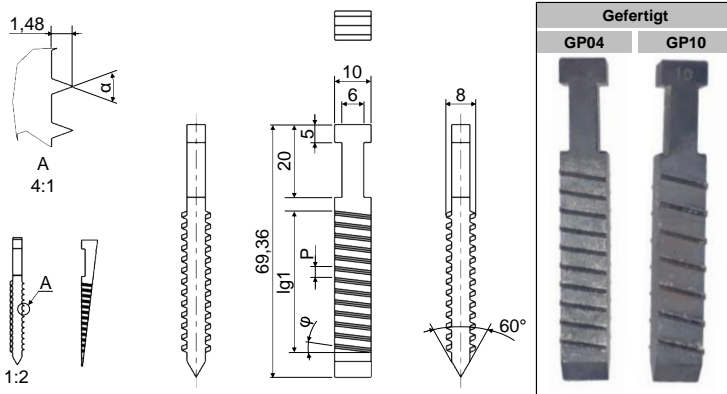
Gewinde-Testobjekt des Experimentalaufbaus zum Schrauben-Testing. Das abgewickelte Gewinde ermöglicht die Untersuchung von Gewindeparametern in spezifischen Richtungen zur Holzfaser. Die zu variierenden Gewindeparameter sind die Gewindesteigung P und der Flankenwinkel α . Übersetzt aus (Hölz, Kleinhans & Matthiesen, 2021)
